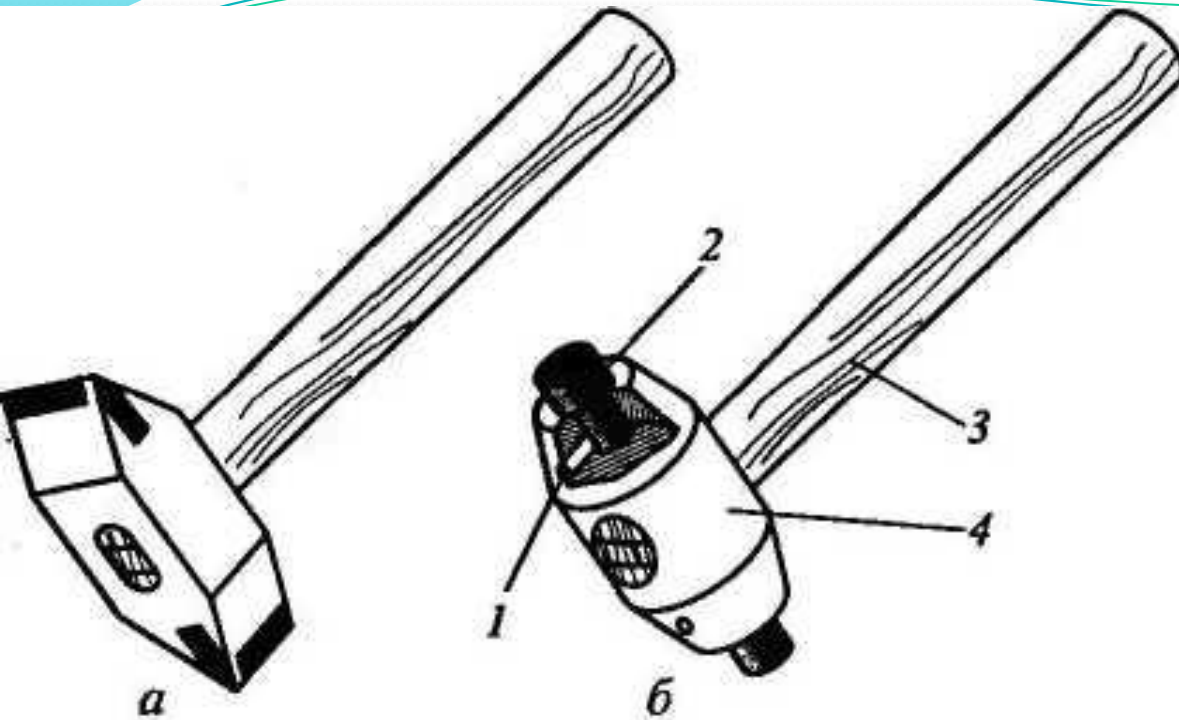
Молотки с мягкими вставками: а - с призматической; б - с цилиндрической: 1 - штифт; 2 - боек; 3 - рукоятка; 4 - корпус
